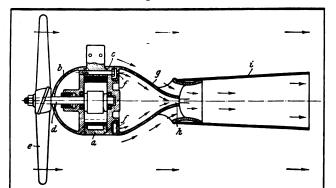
Druckluft-Luttenventilator mit Auspuffstrahldüse.
